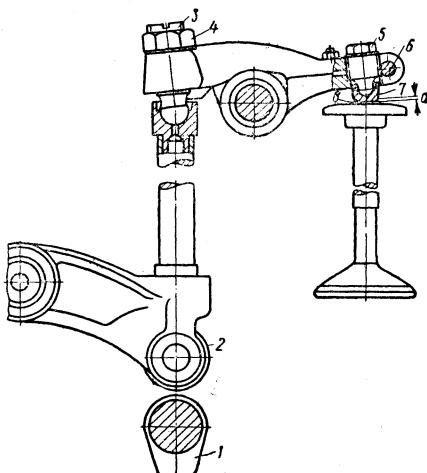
Схема установки зазоров в клапанах на цилиндровых крышках дизеля 2Д50:
